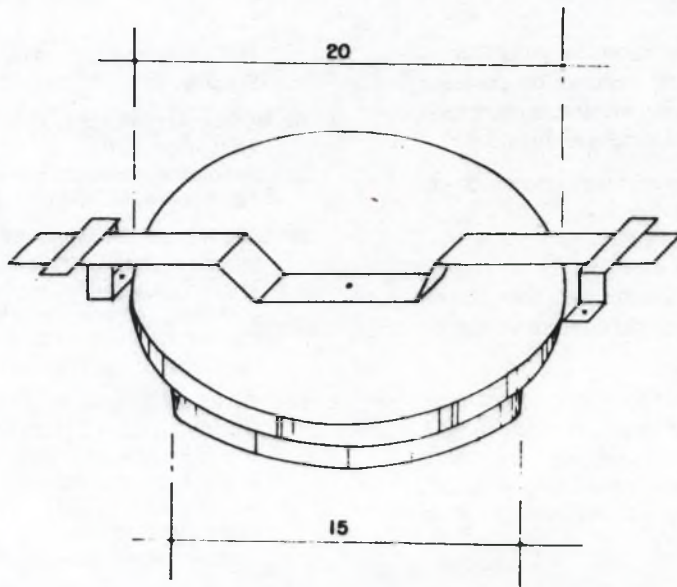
(continuação). Projeto para construção do coletor solar (dimensões em cm)
